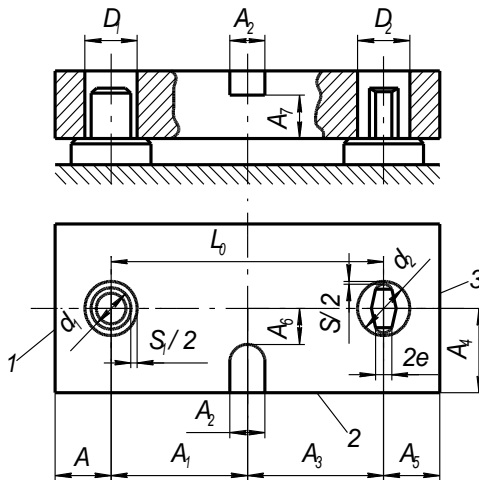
Схема встановлення заготовки при фрезеруванні обробці (до задачі 7).
